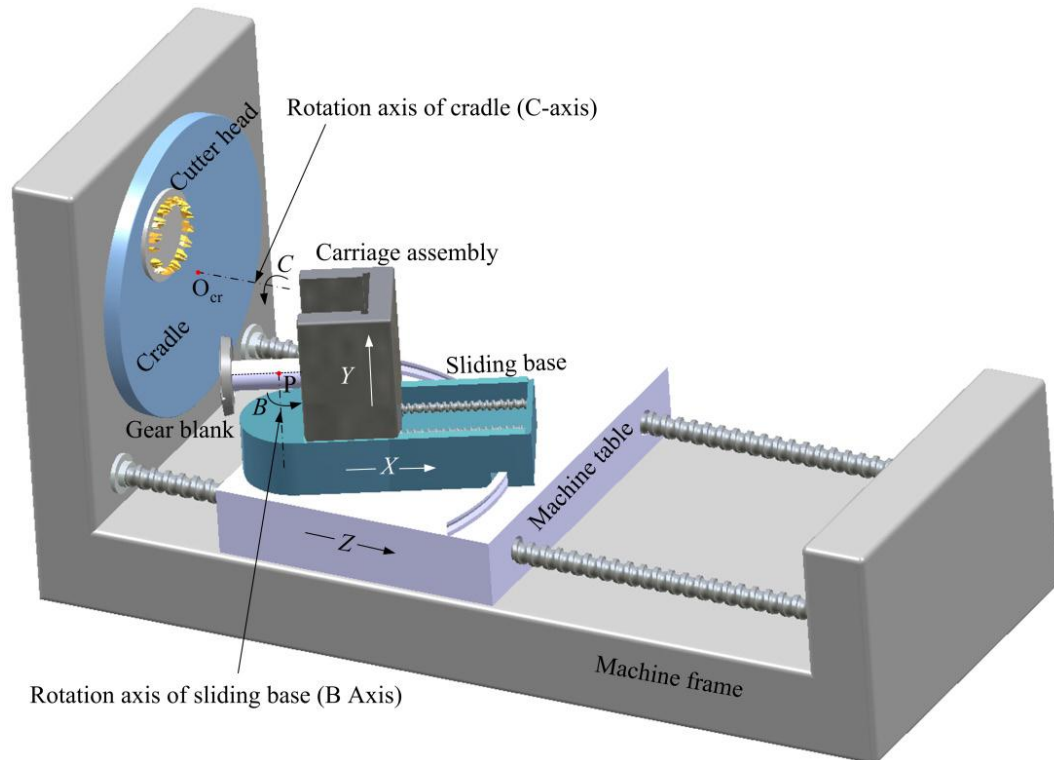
Компановка фрезерного верстата для фрезерування профільних поверхонь деталей машин [22]
